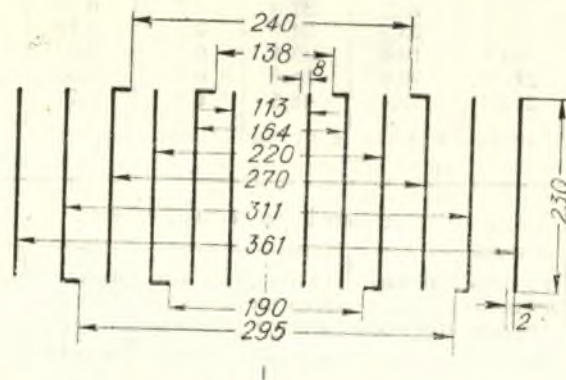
Размеры деталей ротора осадочного сепаратора.
